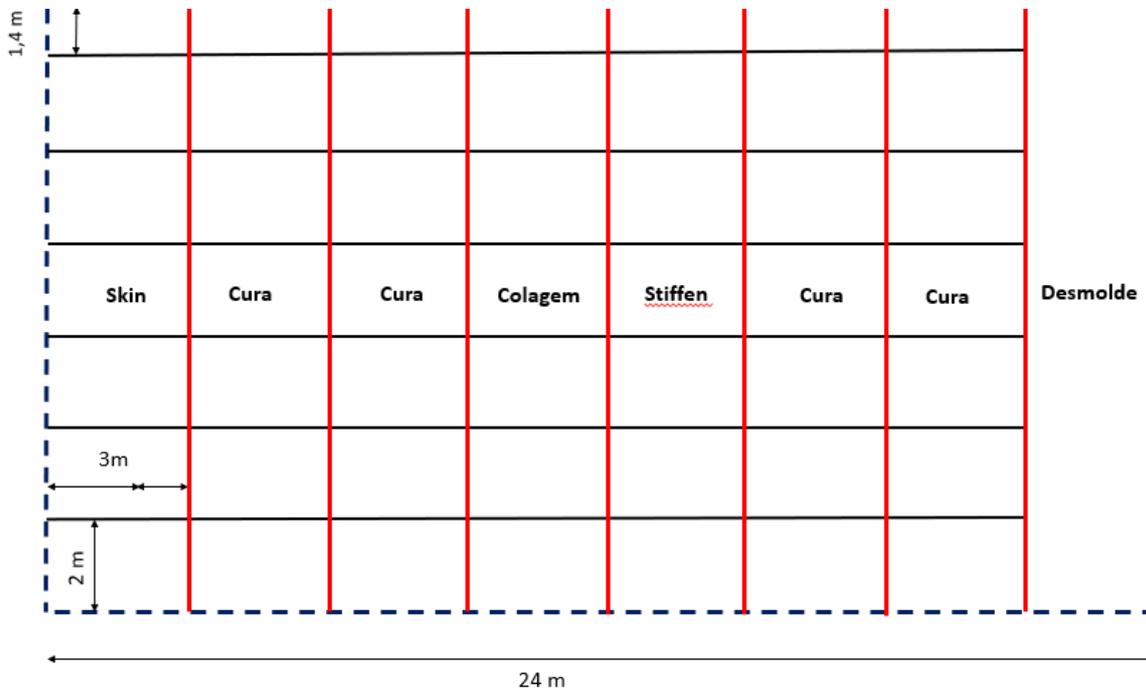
Proposta 2 do layout da zona de laminação e desmolde
